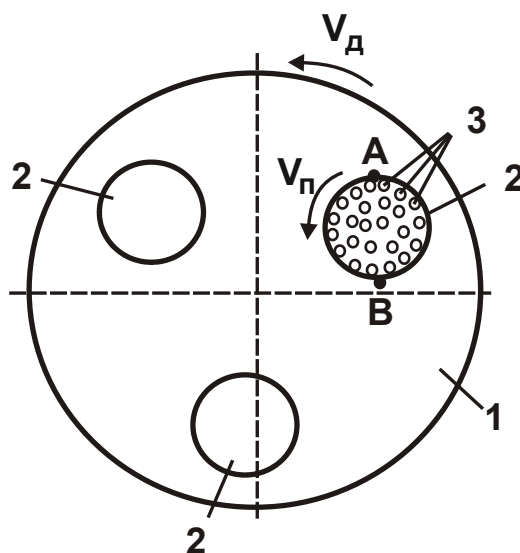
Кинематическая схема притирки торцовых поверхностей колец
